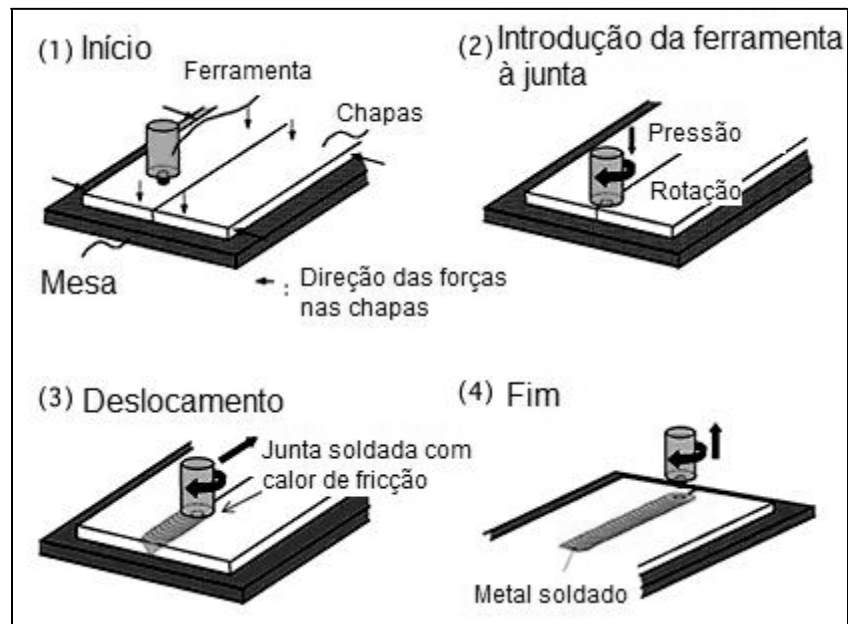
Princípios básicos do processo de soldagem FSW [13].
